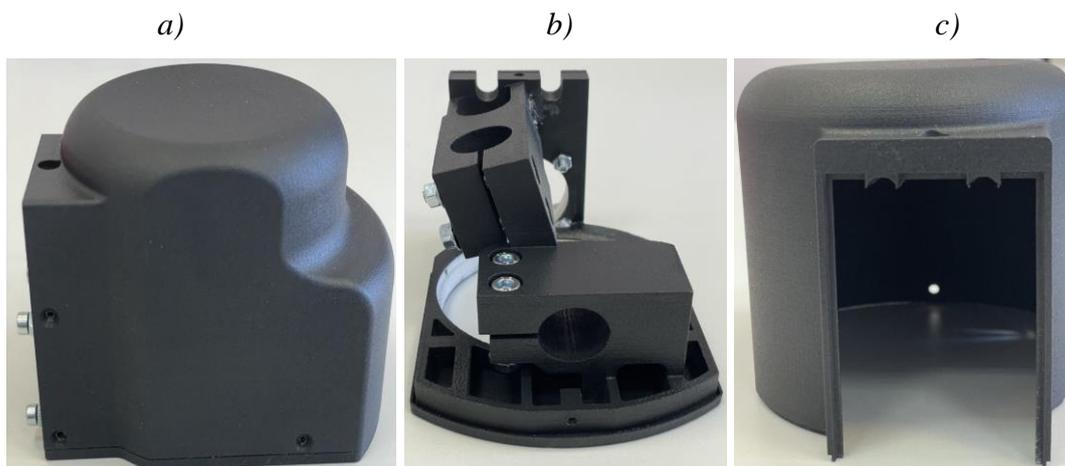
Детали второго опытного корпуса лазерной головки, изготовленные из полиамида ПА 12 на 3D-принтере по технологии SLS: *a)* корпус лазерной головки в сборе; *b)* нижний полукорпус; *c)* верхний полукорпус
